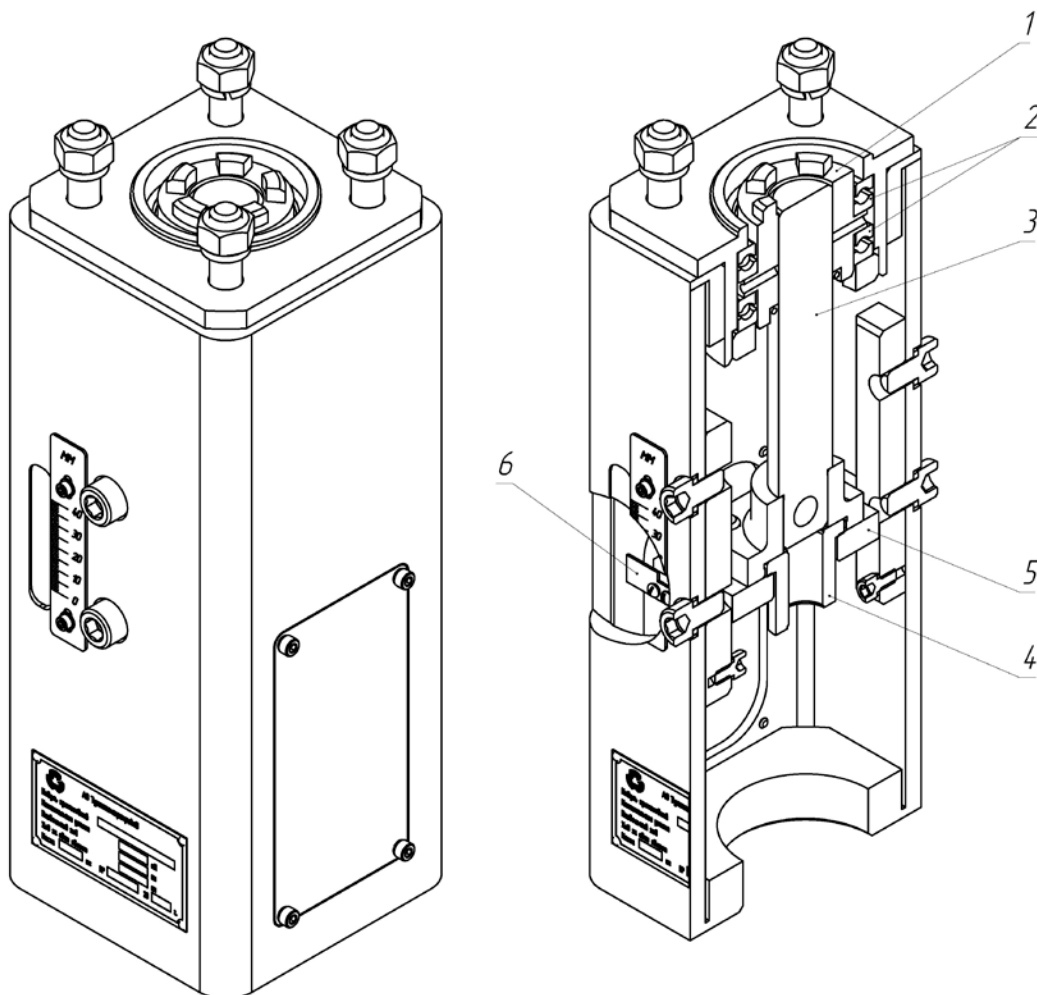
Конструкция модуля (общий вид и разрез)
